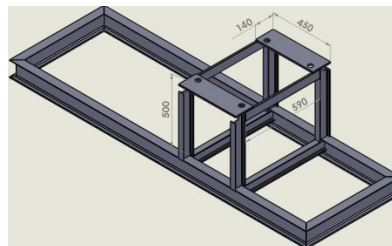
45: Dimensiones de la estructura de la estación de formado
